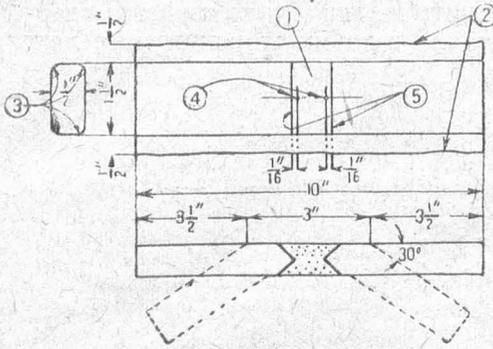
Образец для испытания на свободный изгиб. 1—поверхность шва должна быть обработанной; 2—если образец вырезан газом, то эти кромки должны быть обработаны; 3—углы закруглить на радиус 1,5 мм; 4—следы керна; 5—основание шва
